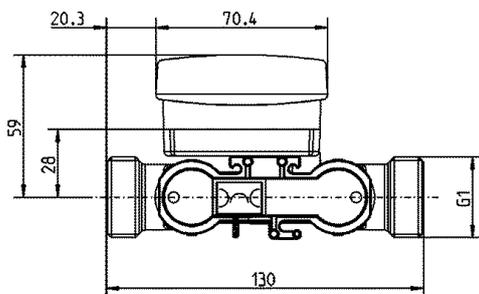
Übersicht Maße Baulänge 130 mm (Gewinde)
